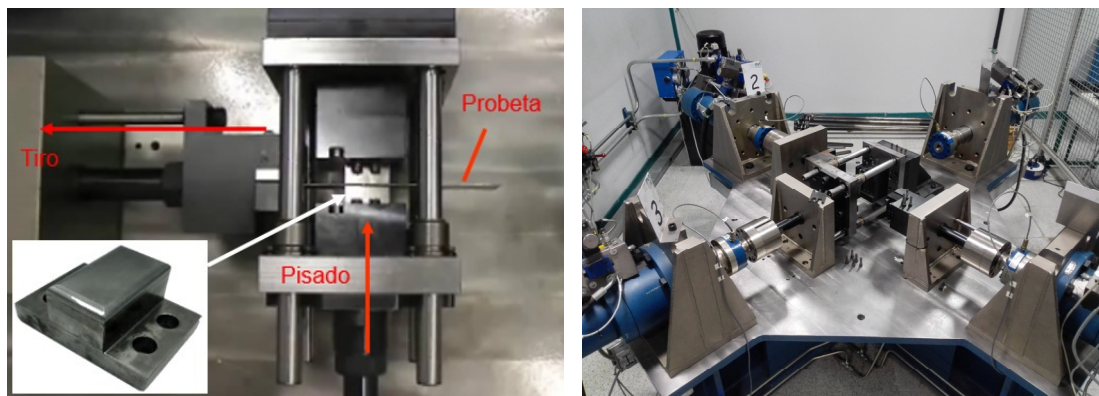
Izquierda: utillaje de Strip Drawing test y detalle de los tacos. Derecha: máquina de ensayo biaxial de la Universidad de Mondragón
